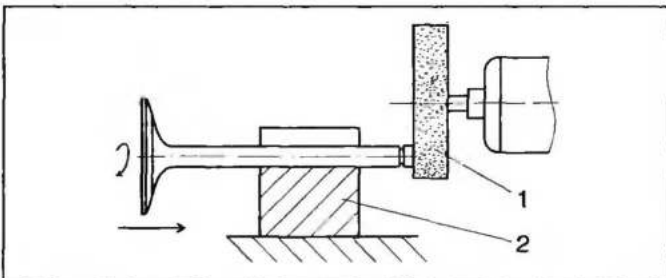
Простой способ ремонта торца клапана: 1 — шлифовальный круг; 2 — призма
